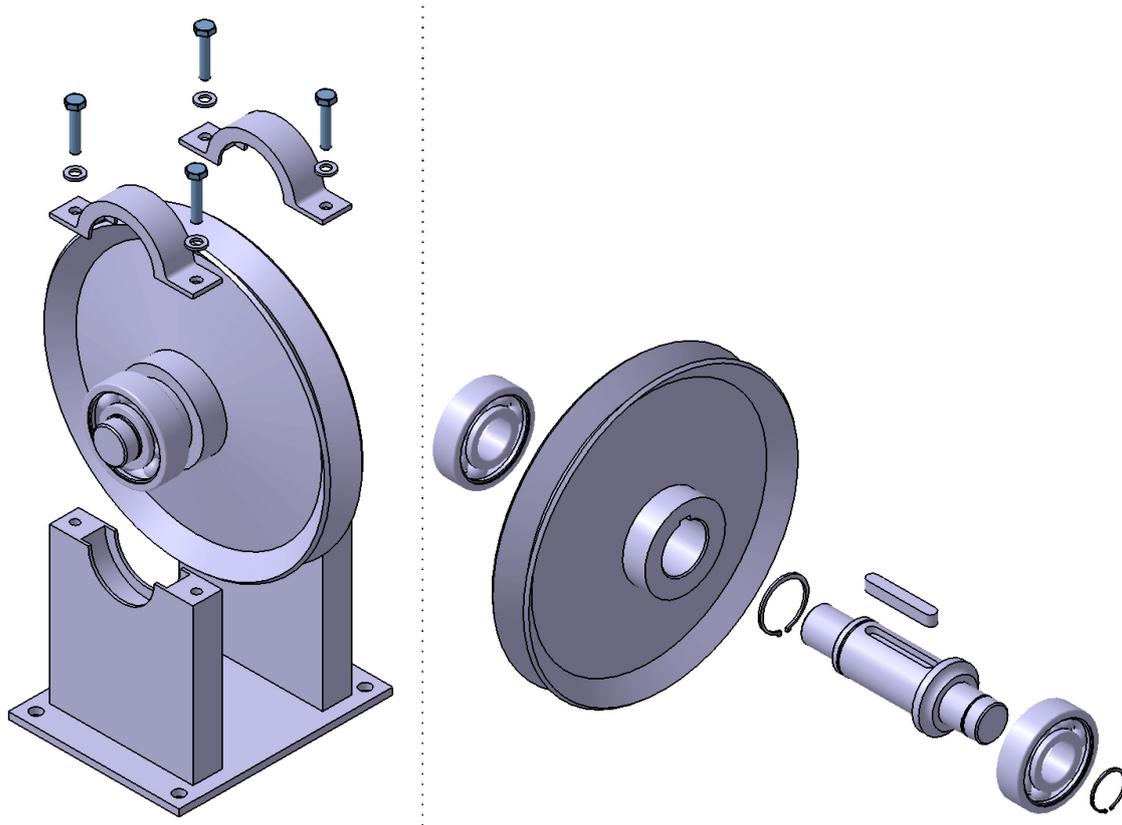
Explosionszeichnung der Seilrollenkonsole und der Wellenbaugruppe
